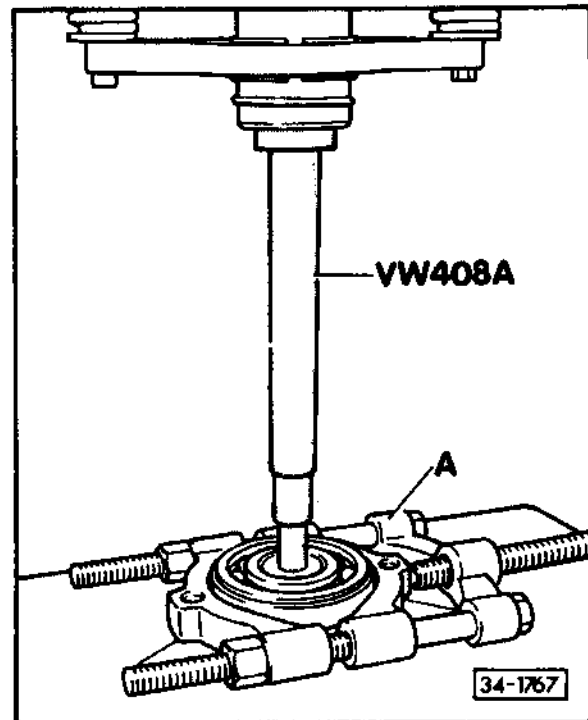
Rillenkugellager für Zahnradwelle abdrücken
